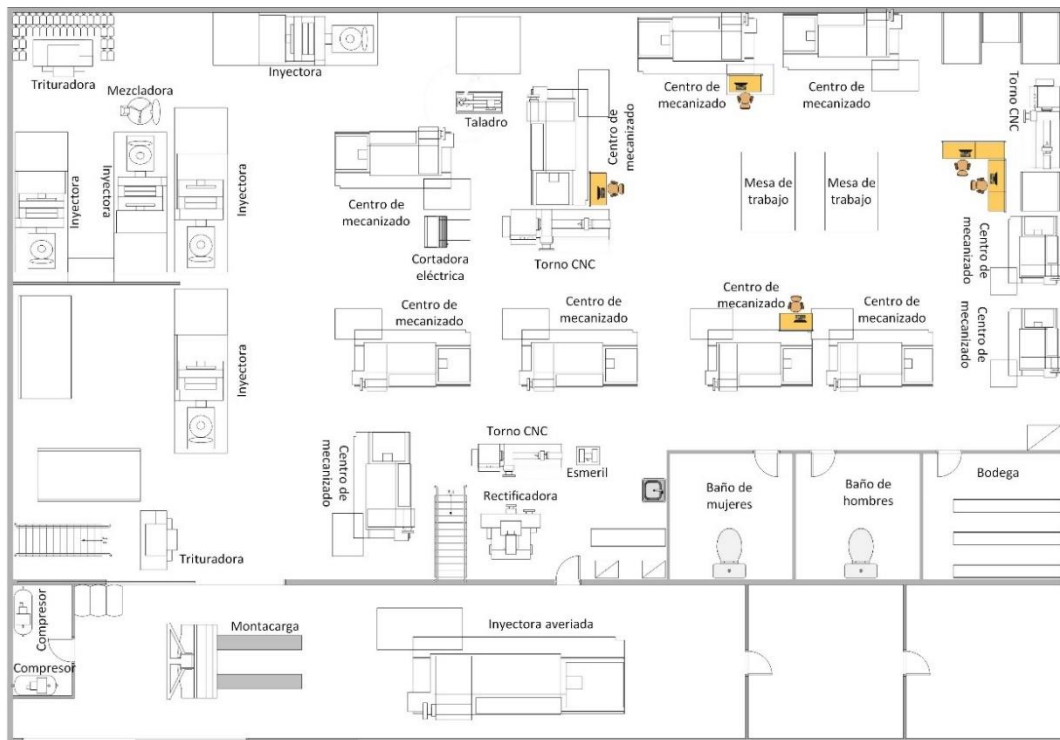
Layout planta principal de producción Multiaccesorios M.G.
